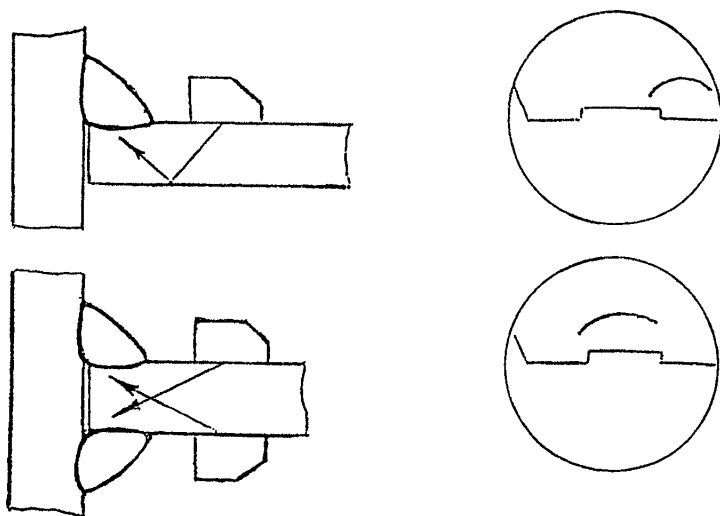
Схемы контроля тавровых сварных соединений, выполненных без разделки кромок
